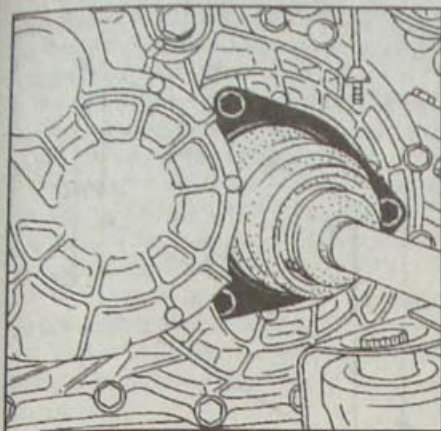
Расположение болтов крепления гофрированного чехла приводного вала на фланце дифференциала
